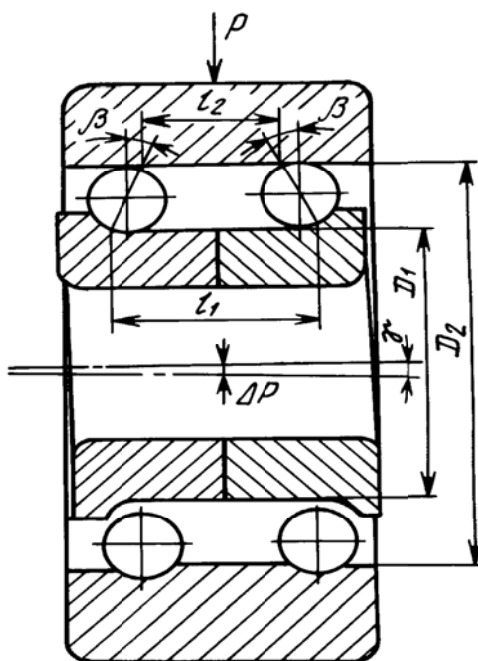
Двухрядный шариковый радиально-упорный подшипник
